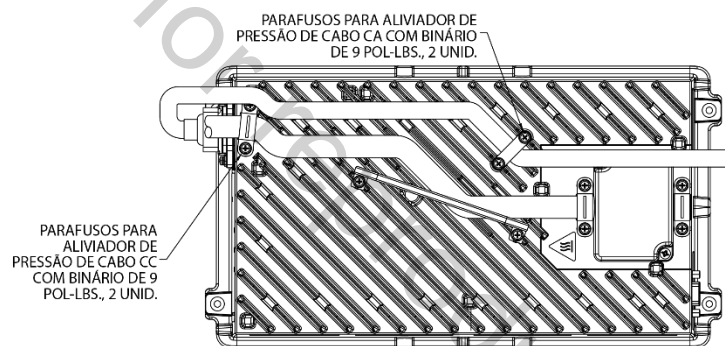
Encaminhamento alternativo dos cabos CA e CC
